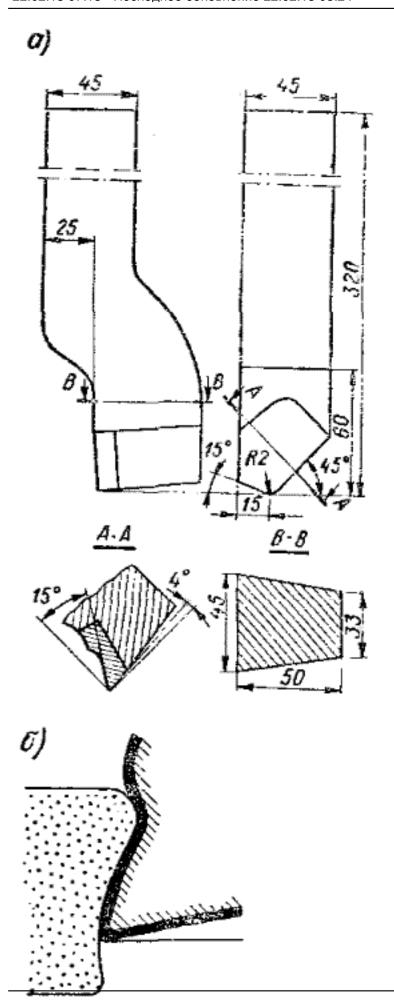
Резец для тяжелых работ конструкции Д. Н. Преснова (а) и схема врезания в металл обычного строгального резца и резца Д. Н. Пресно-
